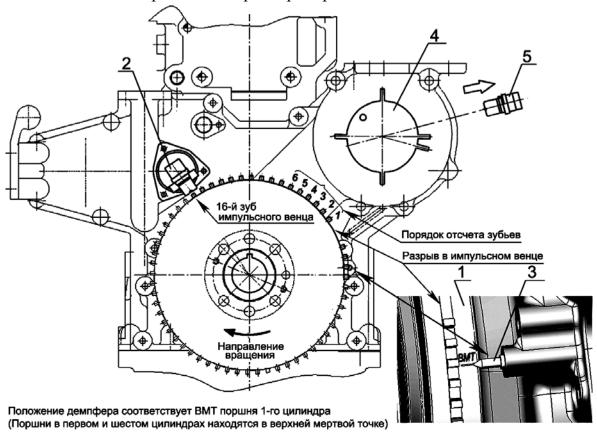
Приспособление для фиксации импульсного венца шестерни привода топливоподкачивающего насоса.
